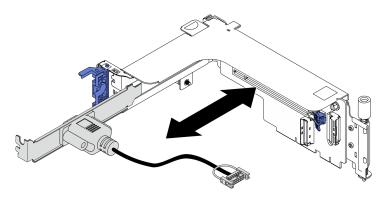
Removendo o módulo de porta serial da placa riser PCIe.
